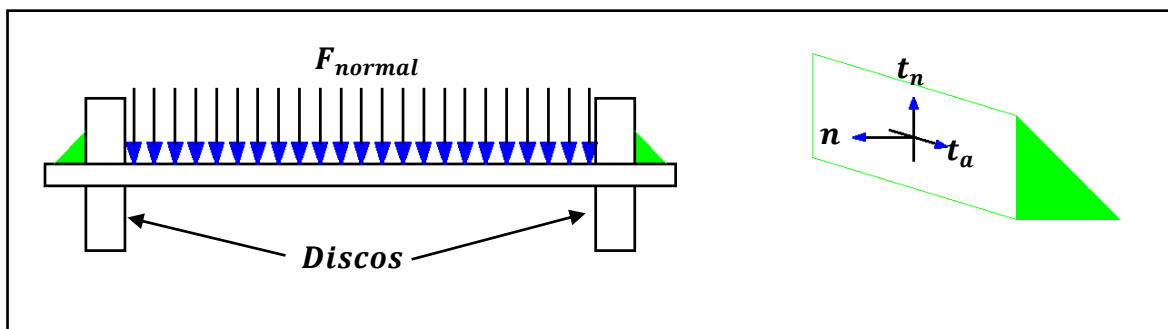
18. Esquema del perfil de soldadura para el alabe con el disco del rotor.
